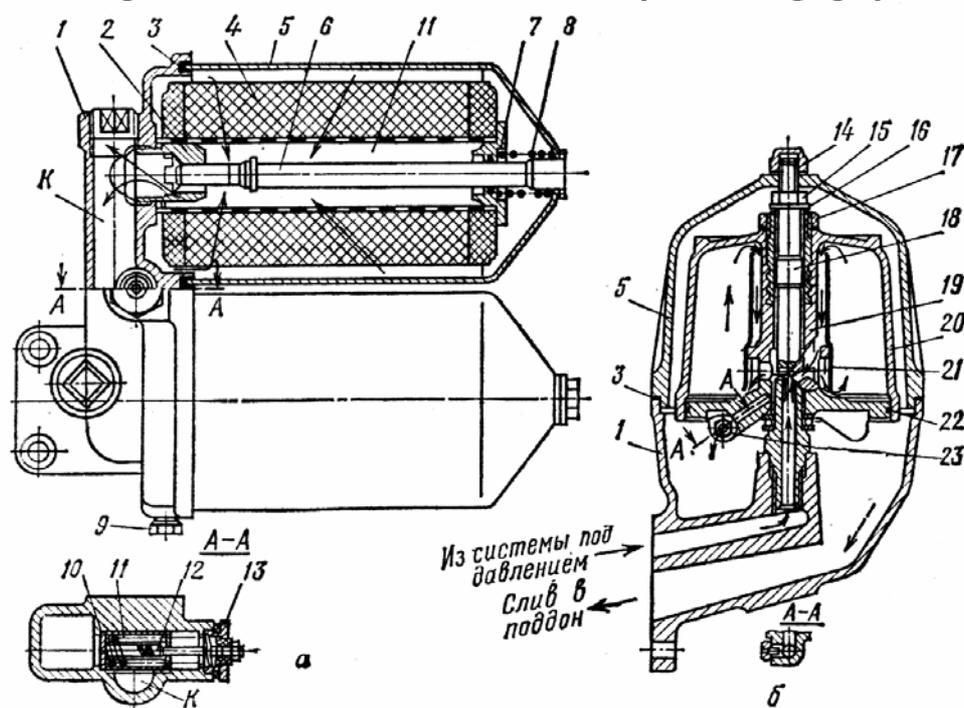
Фильтры двигателя ЯМЗ-240Б:
